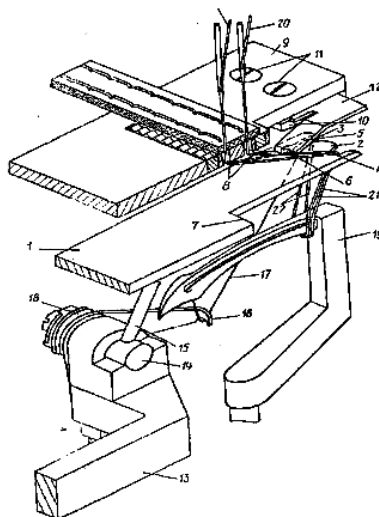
Приспособление для обрезки нитей игл и петлителя.
